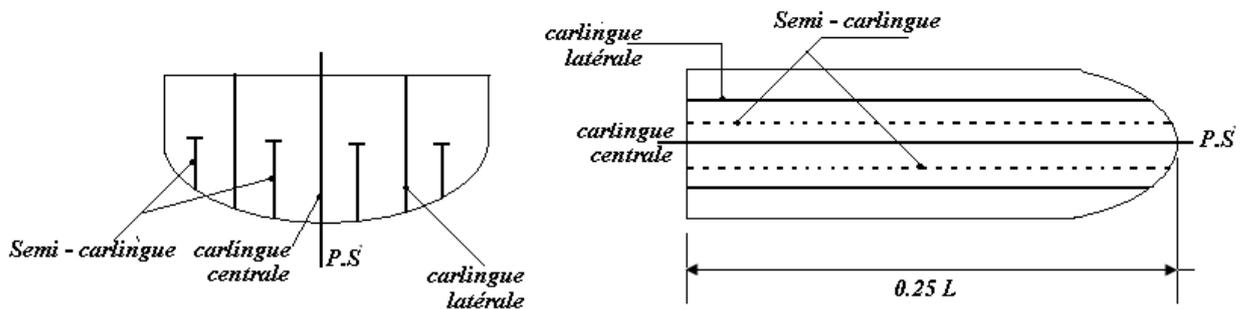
Construction de la carlingue latérale avec semi-carlingue à $0.25 L$ de l'étrave.
